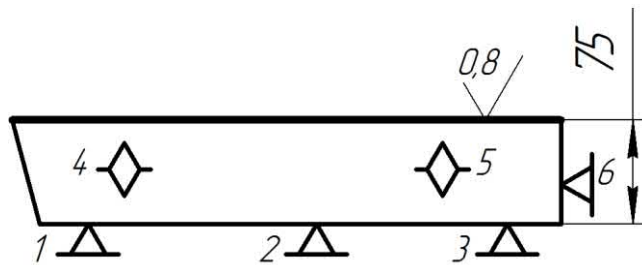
Ескіз обробки і схема базування на операцію 065
